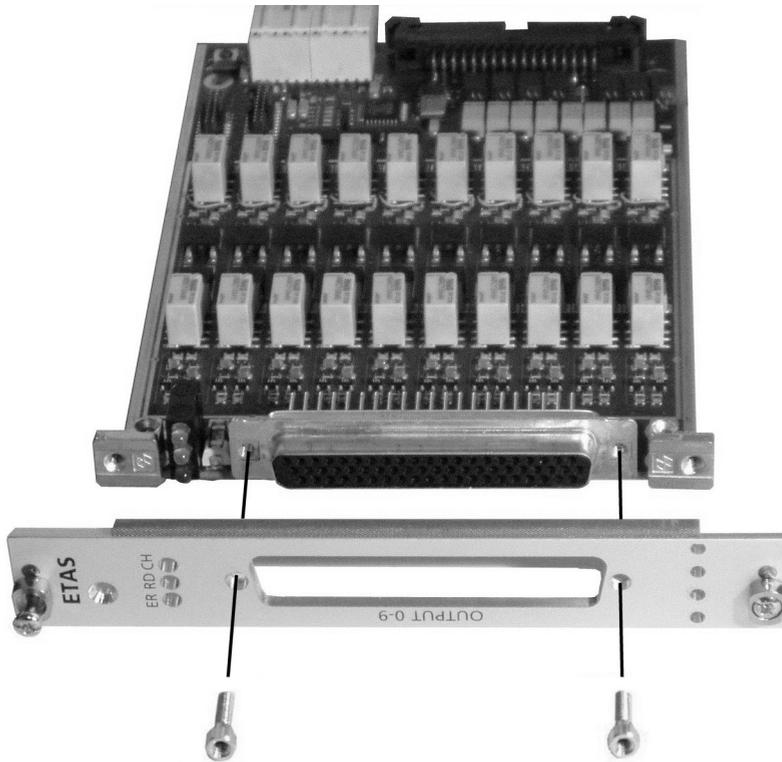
Befestigung der Frontplatte am Steckverbinder
